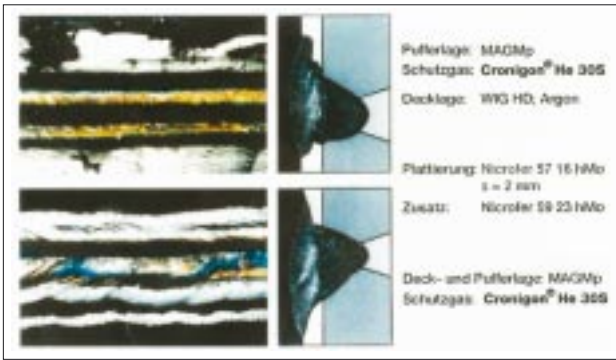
REA-Rauchgasabsorber, Schweißen von plattierten Blechen in Pos PC
